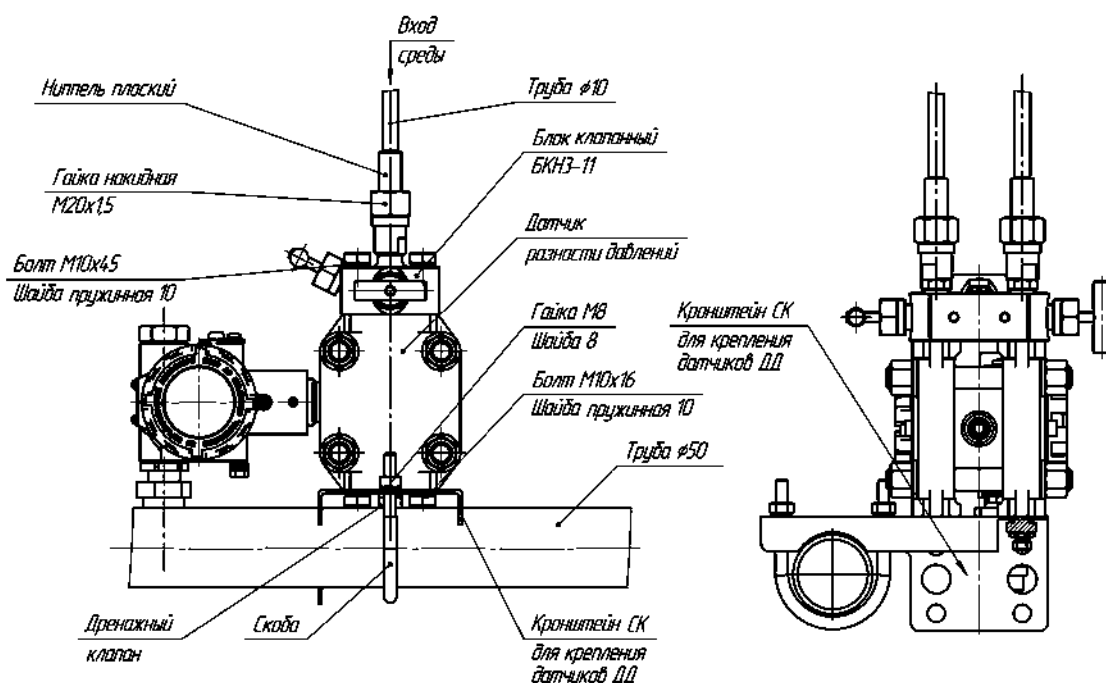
Монтажный чертеж установки преобразователя давления фланцевого конструктивного исполнения с монтированным клапанным блоком «БКН» резьбового присоединения к импульсным линиям, и с КМП «Фланец М20» и «Кронштейн СК» (для крепления датчиков ДД). Вариант крепления на горизонтальной трубе Ø50.
